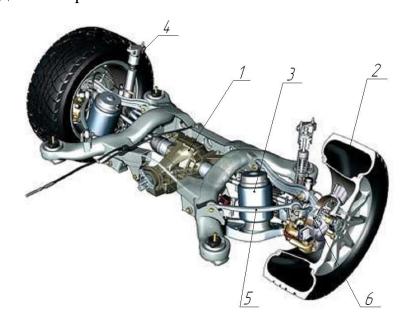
Подвеска «Де Дион»: 1 — редуктор заднего моста; 2 — колесо; 3 — пневматическая камера; 4 — пневмостойка амортизатора; 5 —реактивная штанга; 6 — ступица
